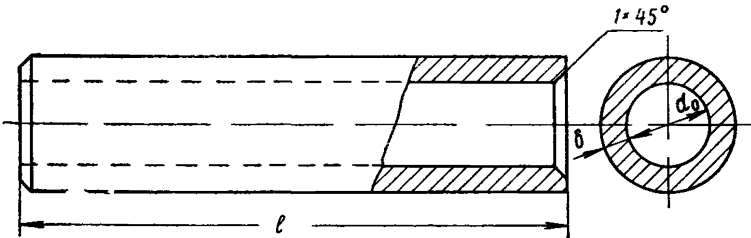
Конструкция и обозначение размеров дополнительных трубчатых элементов — гильз для контактной стыковой сварки высокопрочной арматуры либо прядей
